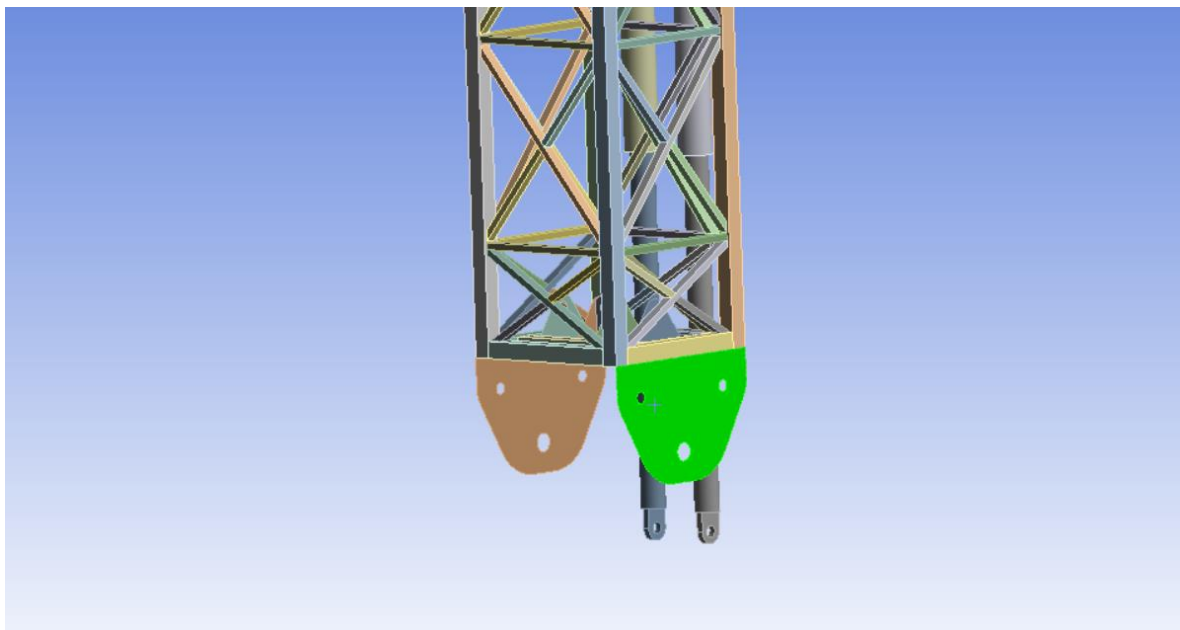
Porovnání vybraných těles 3D geometrie a skořepinové geometrie
